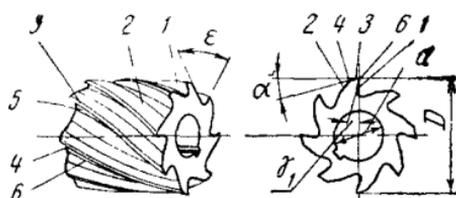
Поверхности и режущие кромки зубьев фрезы
